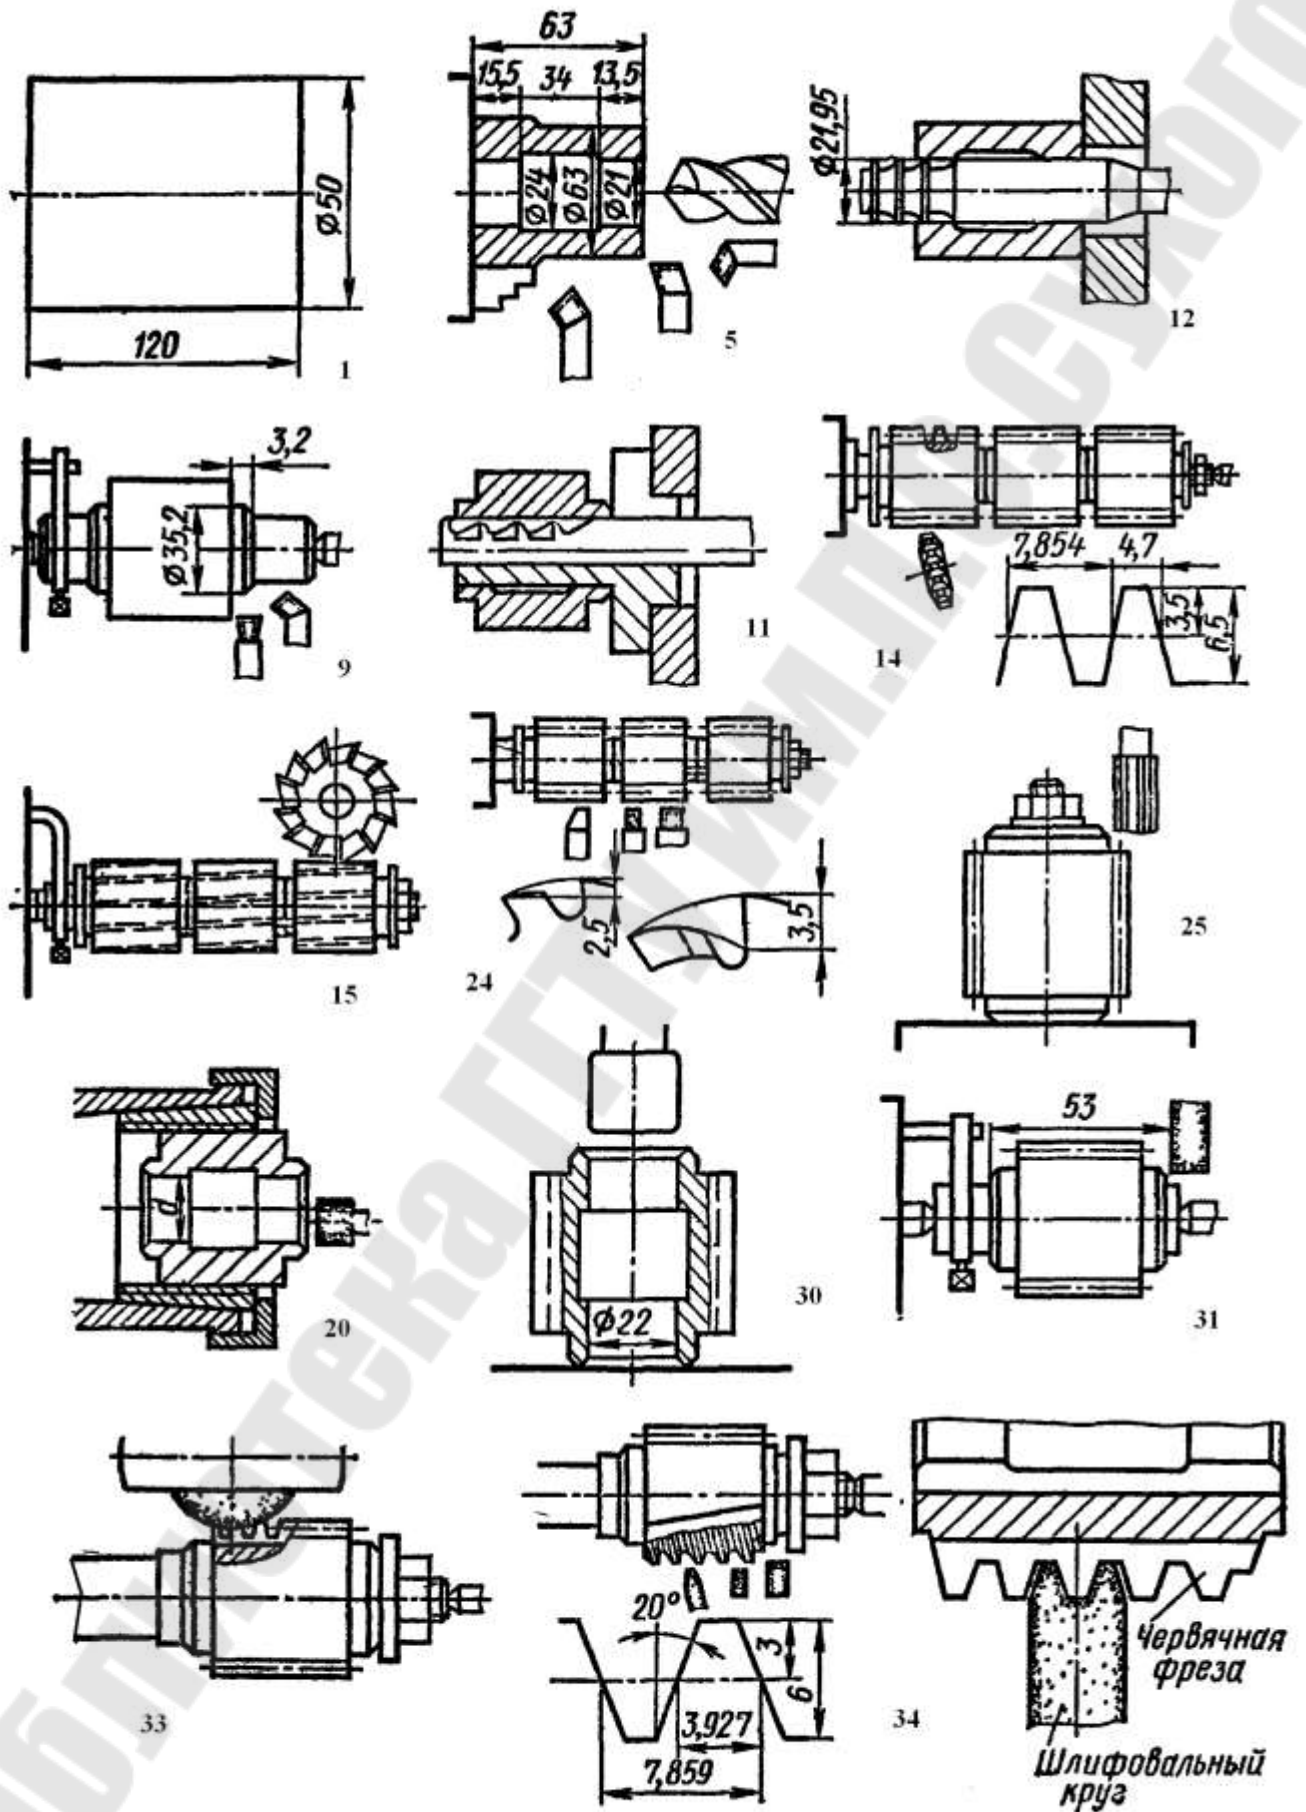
Эскизы к технологическому процессу изготовления червячной фрезы
